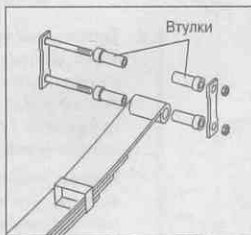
Листовые рессоры оборудованы резиновыми втулками
